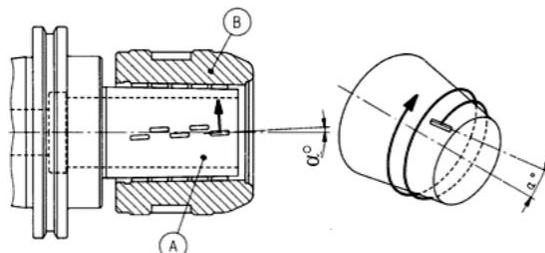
Силовой патрон: А – внутренняя поверхность; В – наружная обода патрона, α° - угол расположения ролика к оси
